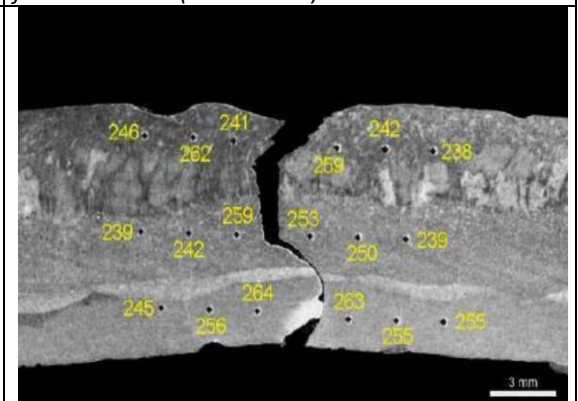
Mediciones de dureza Vickers sobre probeta de la fisura transversal a la soldadura. (Fuente TGP)
